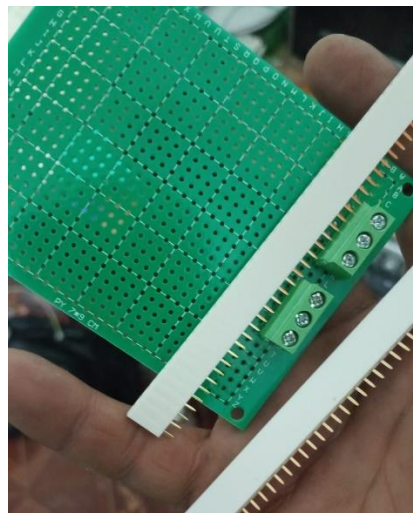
Placa universal para soldadura de componentes eléctricos
